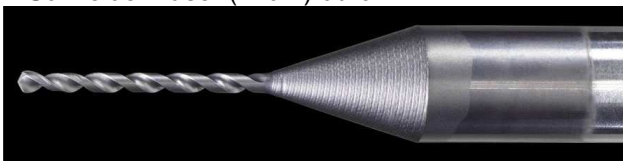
Diamant beschichteter Bohrer - GCT Typ 1638
